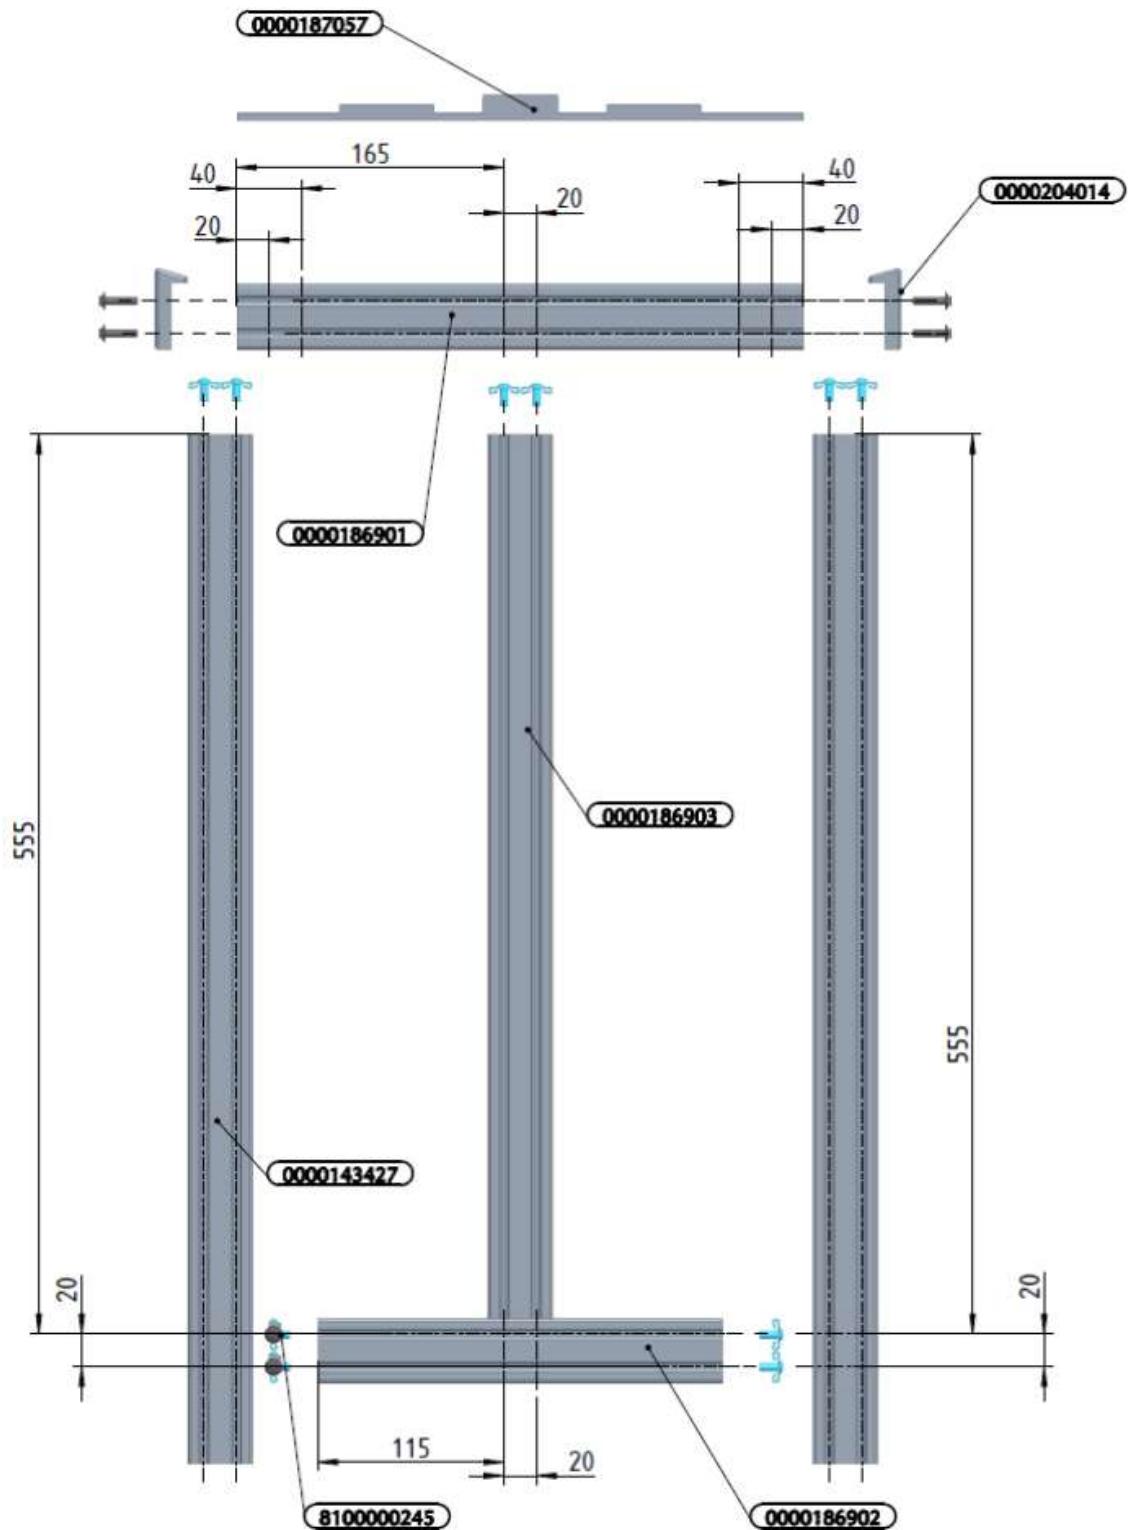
Bohrpositionen am rechten Seitenrahmen
